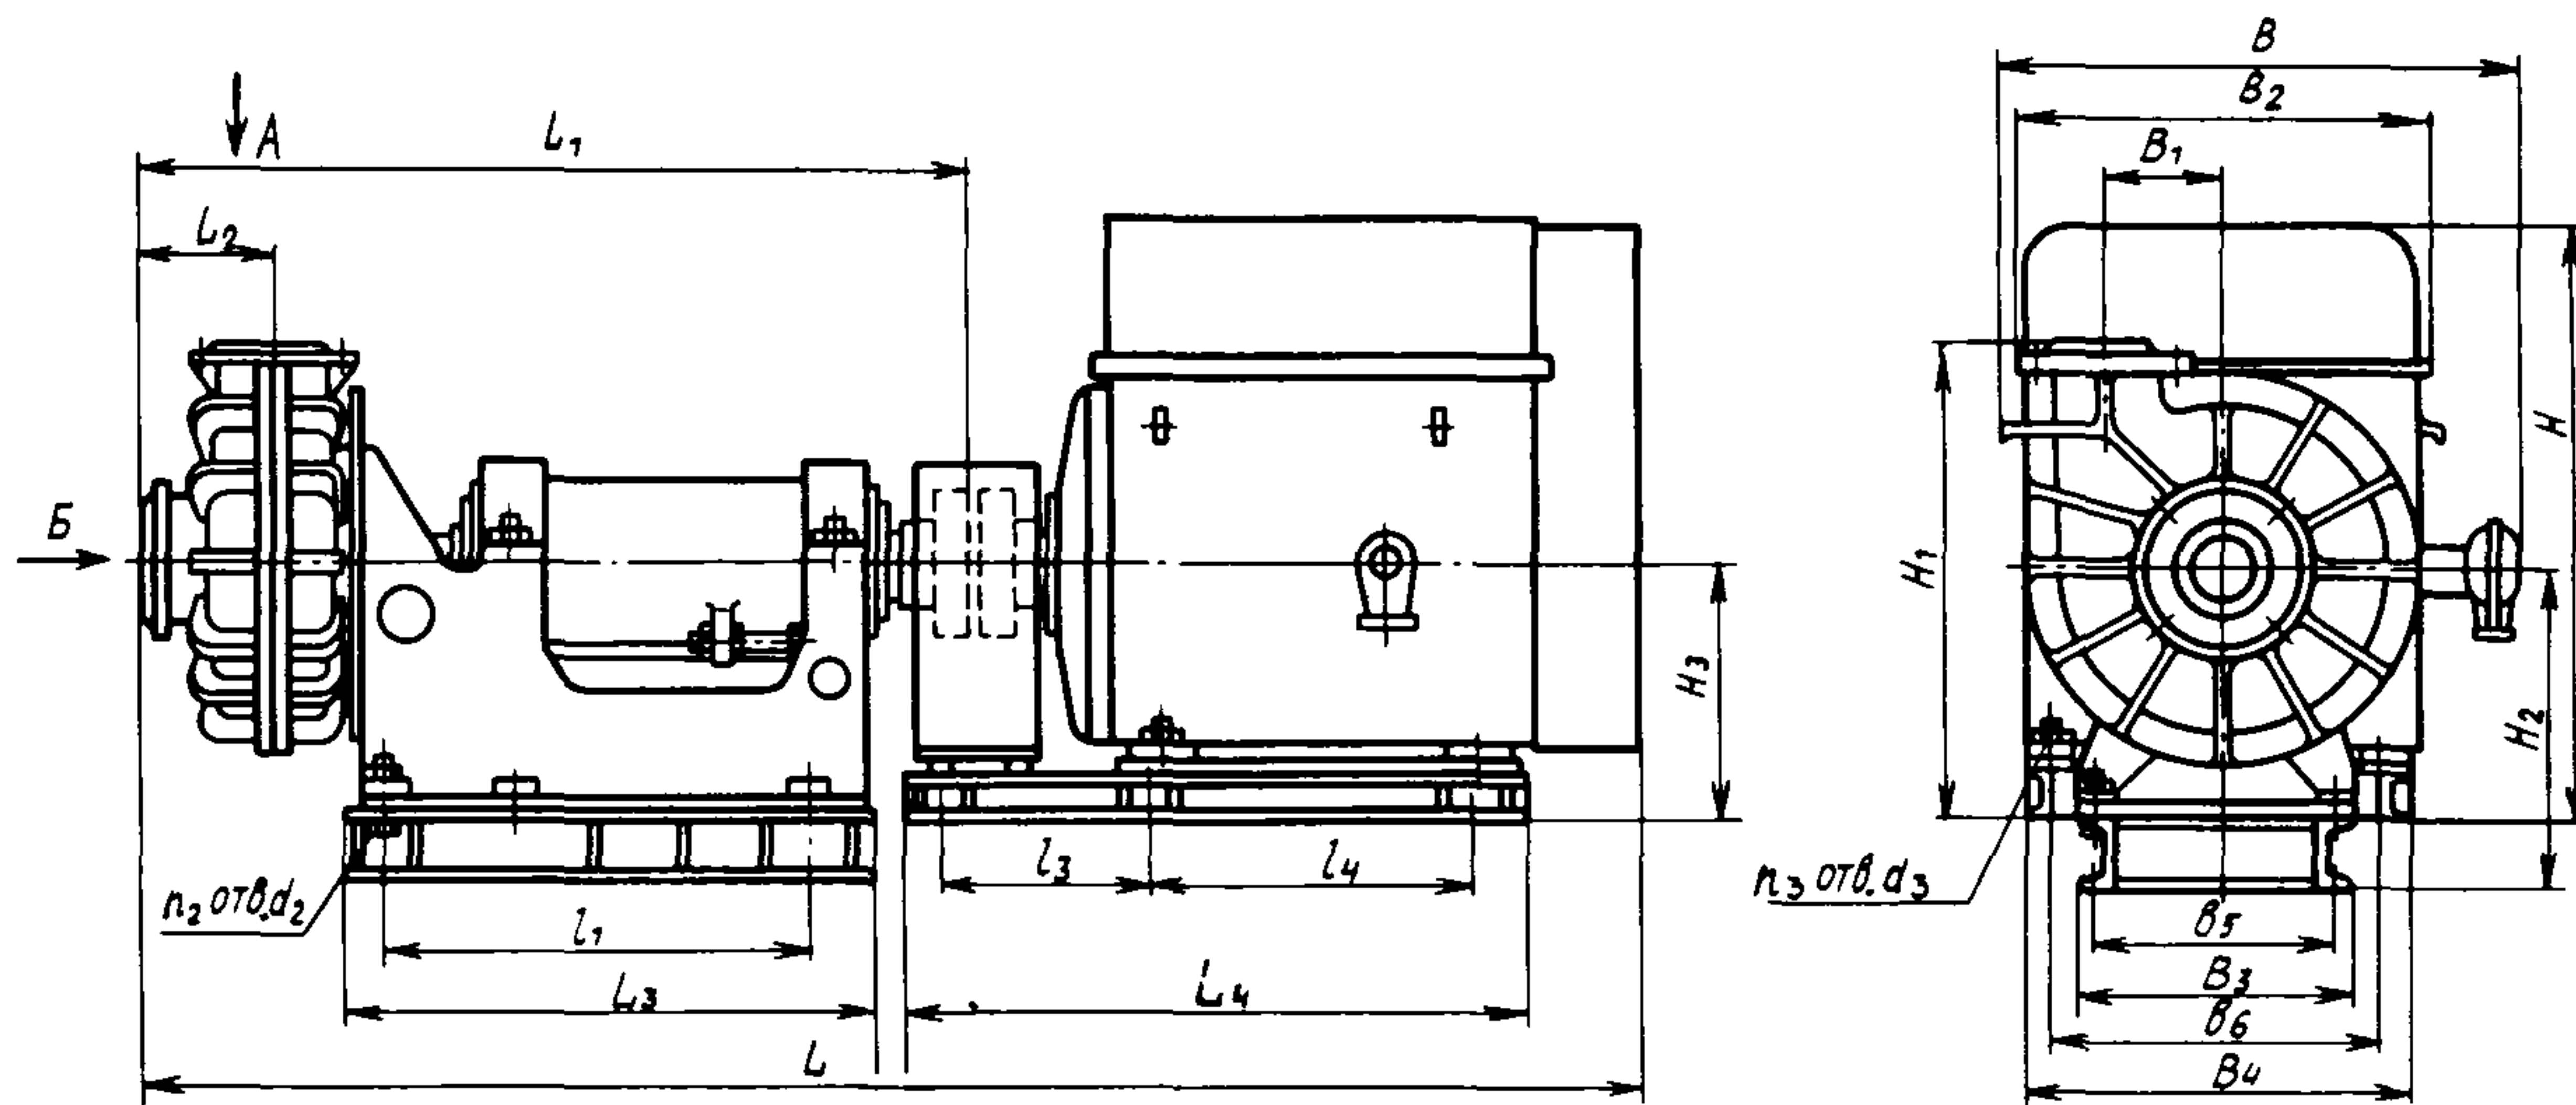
Габаритный чертеж электронасосного агрегата типа ГрА с приводом через упругую муфту
